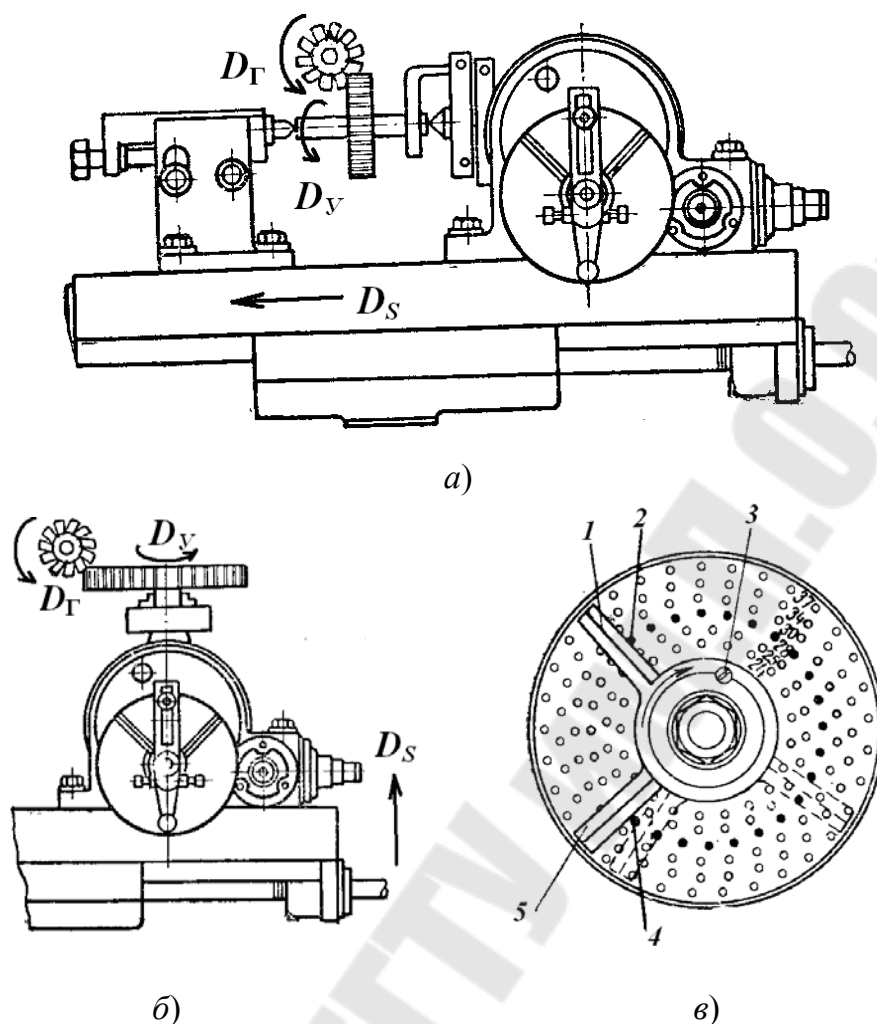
Схемы закрепления и обработки зубчатых колес на горизонтально-фрезерном станке:
